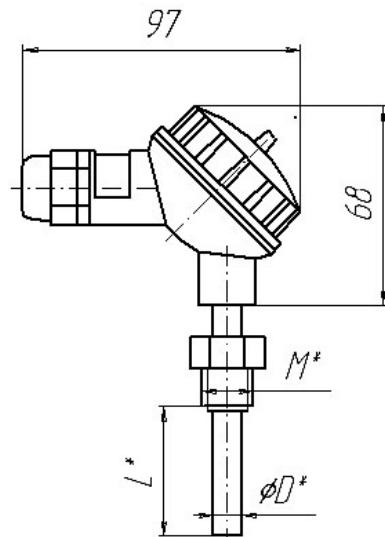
Габаритные и присоединительные размеры датчика ДТ1-DN
